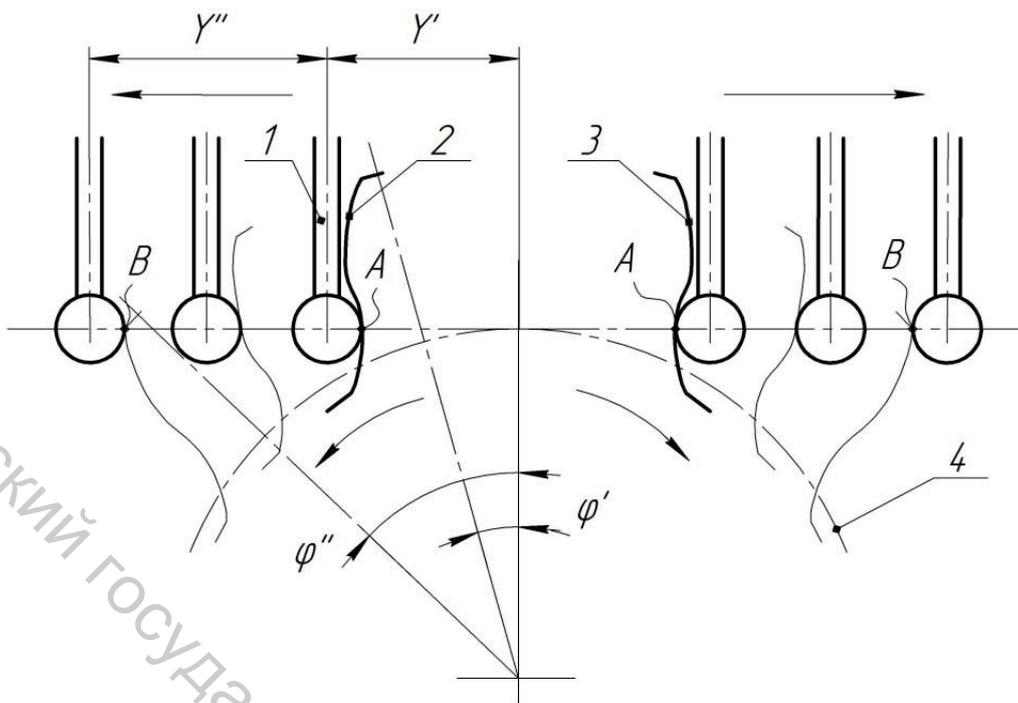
Схема контроля зуба цилиндрического зубчатого колеса
